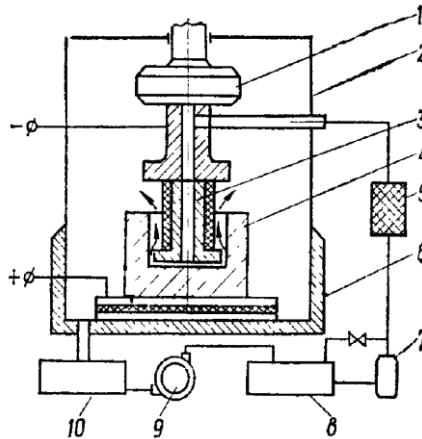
Схема установки для електрохімікогідравлічної обробки
